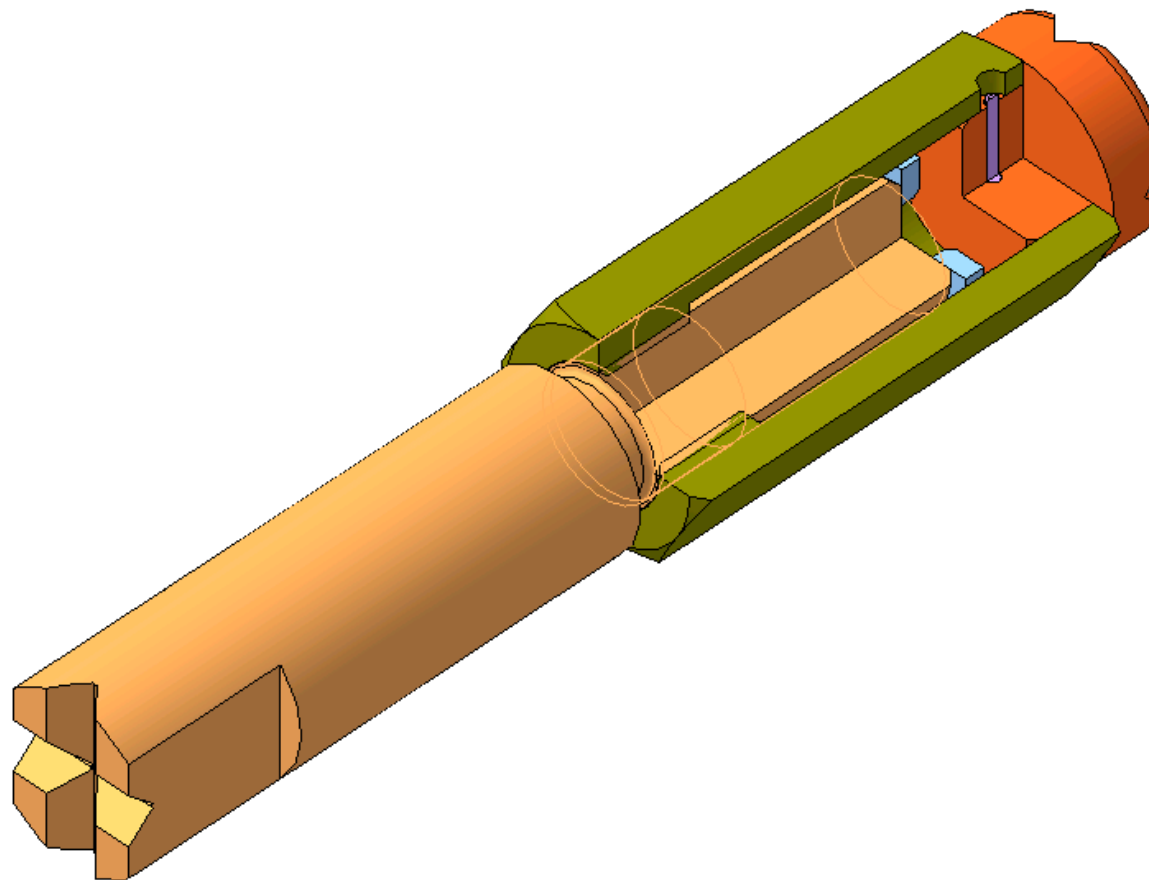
3D-модель сборки изделия «Распорка винтовая» (варианты 19, 39)
